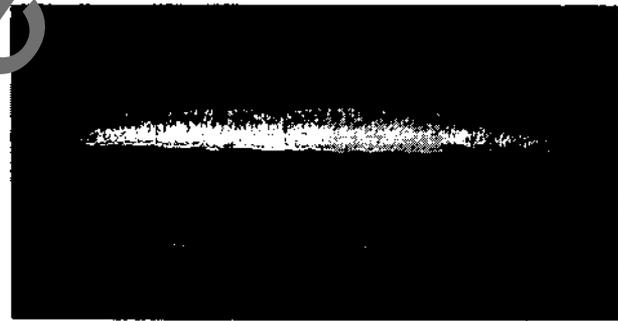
Makroschliff einer UP-Bandauftragschweißung (1:1).
